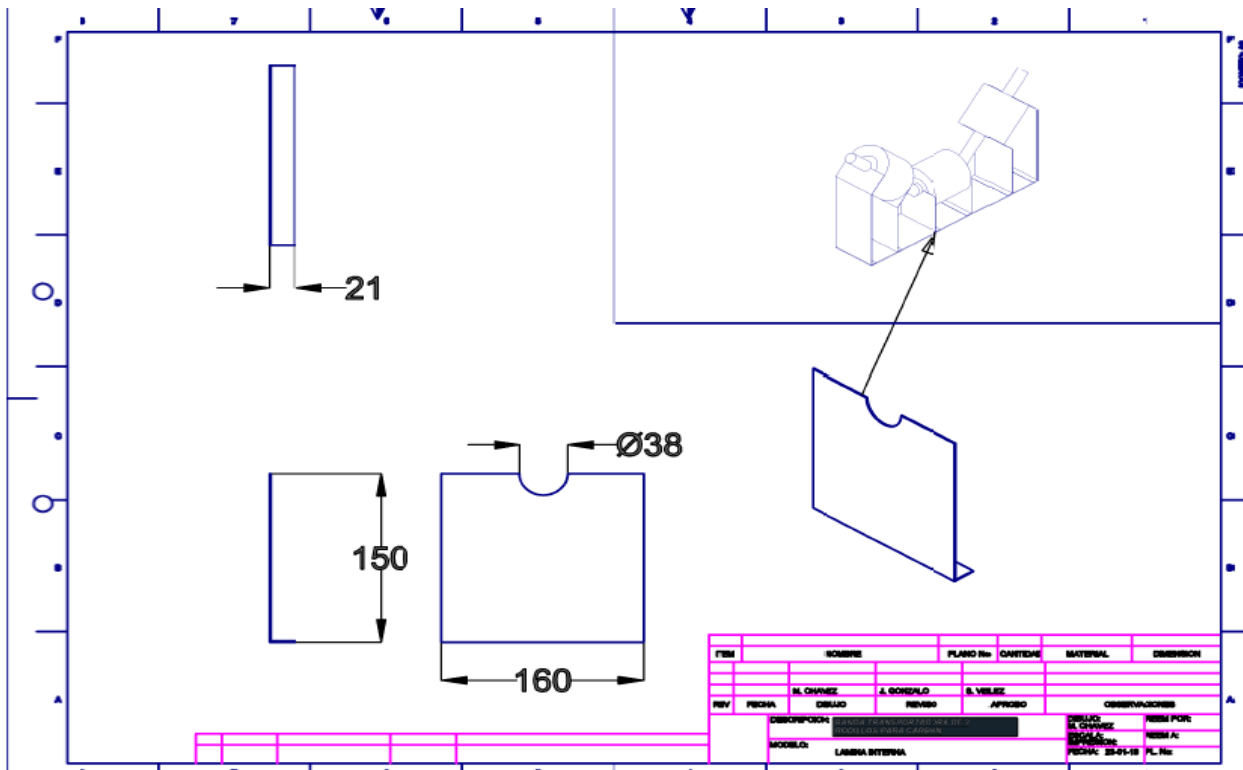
Plano detallado de las láminas verticales de soporte del rodillo principal
